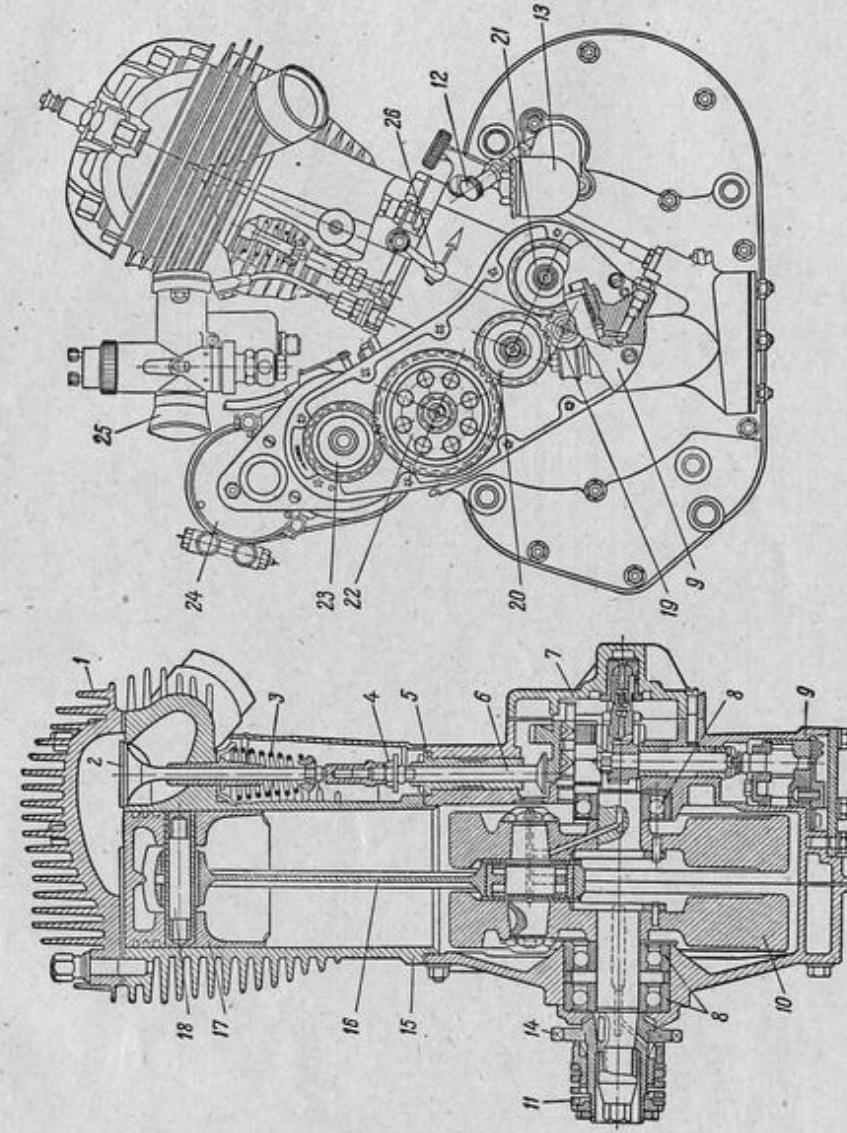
Четырехтактный одноцилиндровый двигатель ГАЗ-АМ-600 объемом 600 см³:
